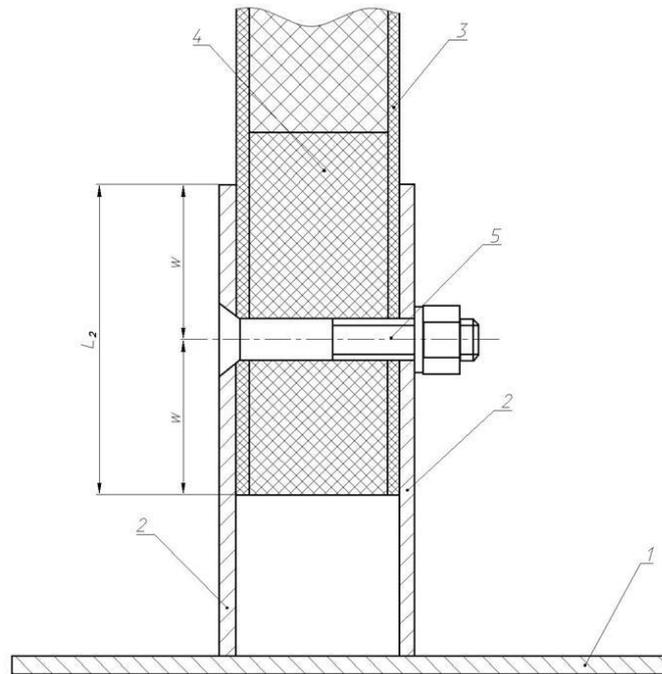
Вузол клеєболтового з'єднання перегородки з металевим корпусом
